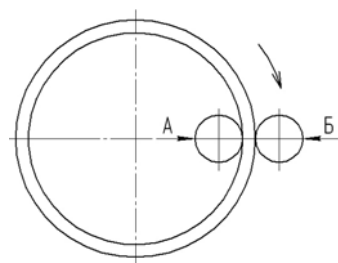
Схема разделения труб на кольцевые заготовки двумя роликами
